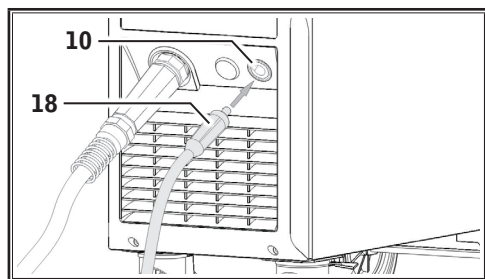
Подключение кабеля для заземления обрабатываемой детали
